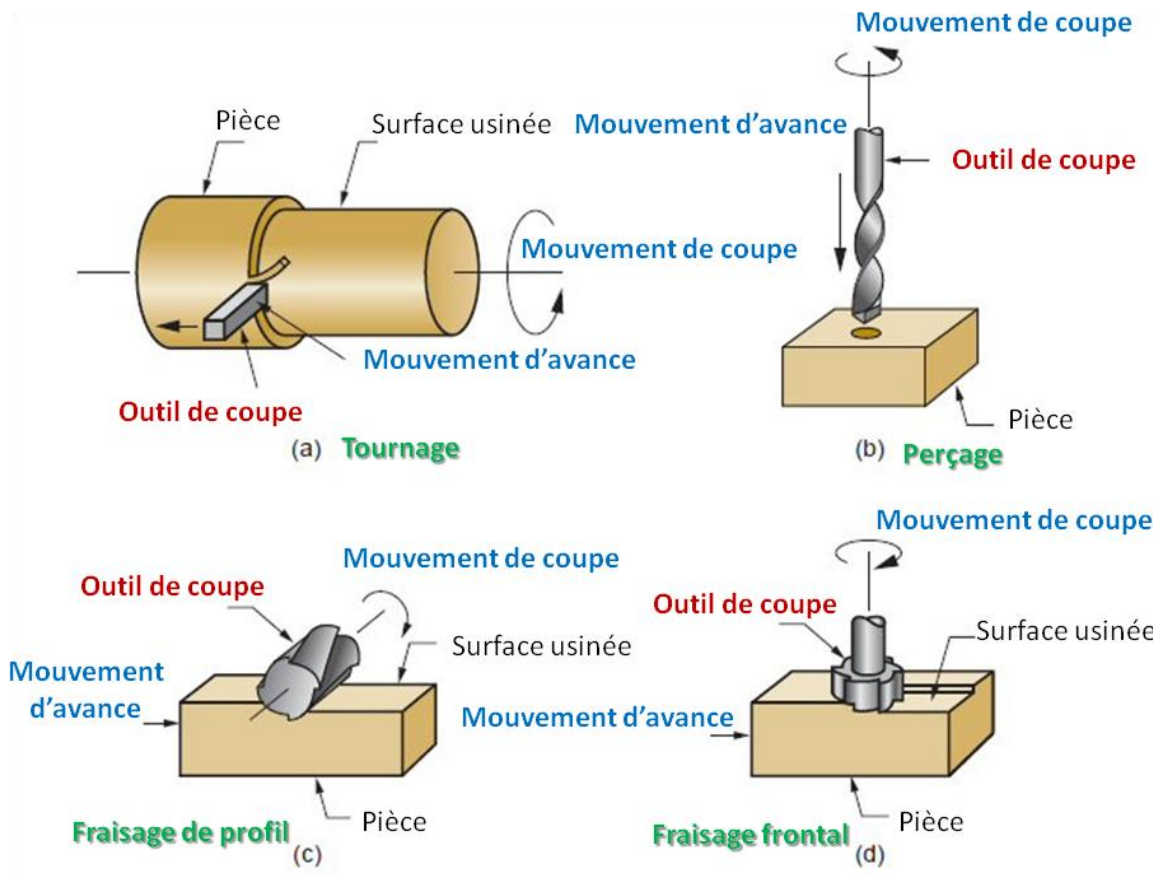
procédés d'usinage : tournage, perçage, fraisage de profil et fraisage frontal
